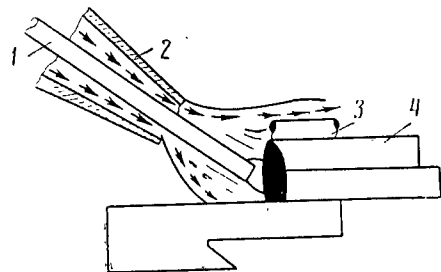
Дуговая сварка обмотки таты с коллектором
